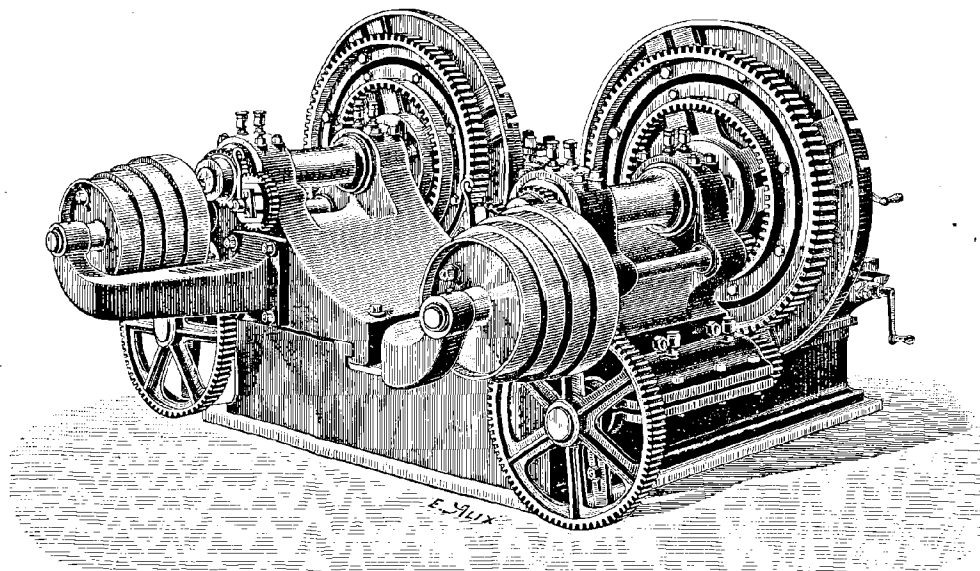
Tour double à plateaux dentés. Vue par derrière.
